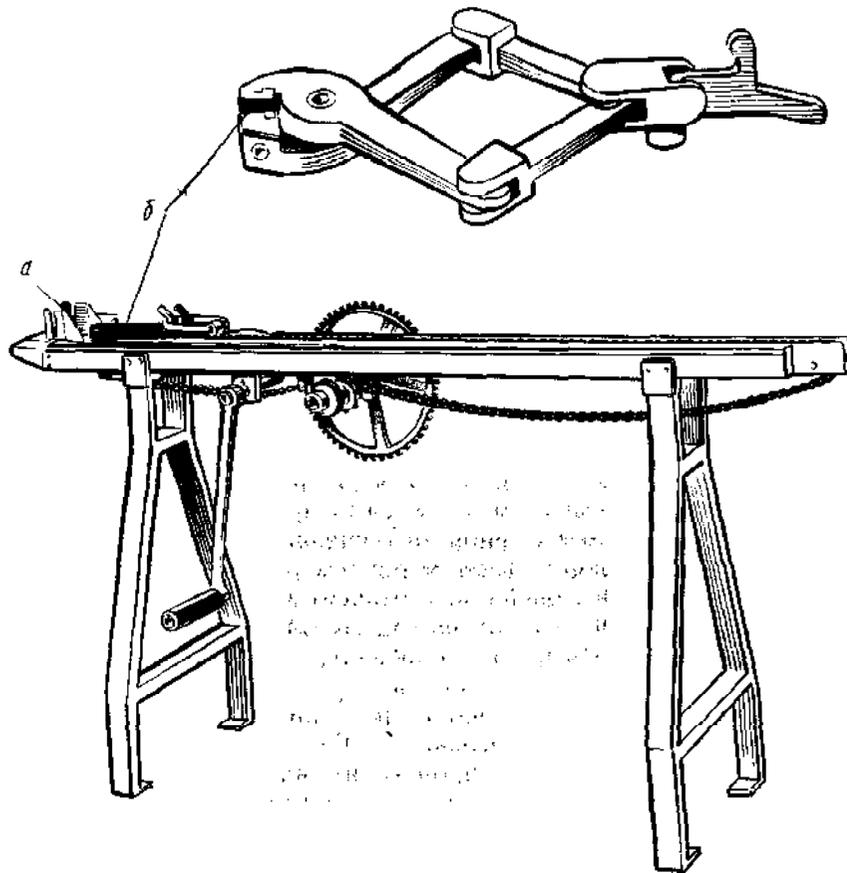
Станок с цепным приводом для протяжки трубчатой заготовки:
